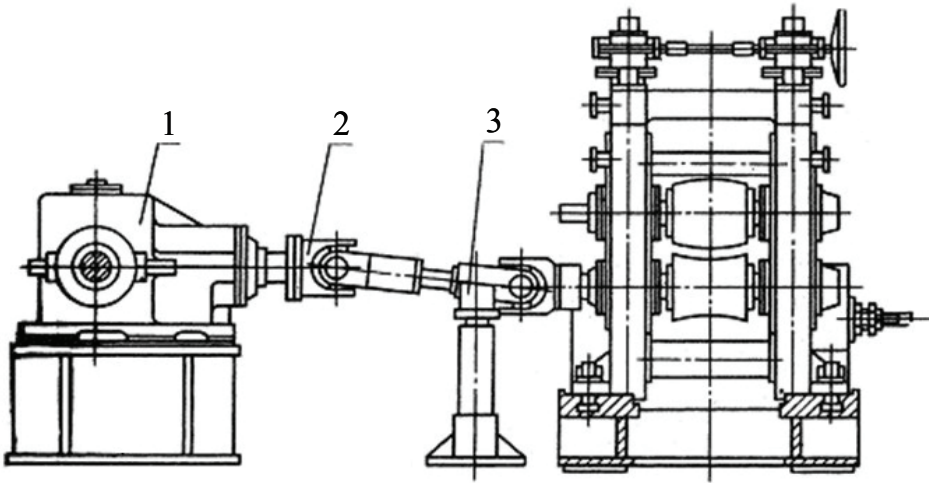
Клеть формовочного стана с приводным нижним валком:
